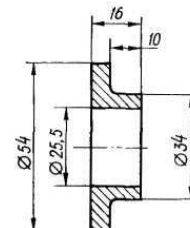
Оправка для напрессовки подшипника и грязезащитного кольца на полуось
